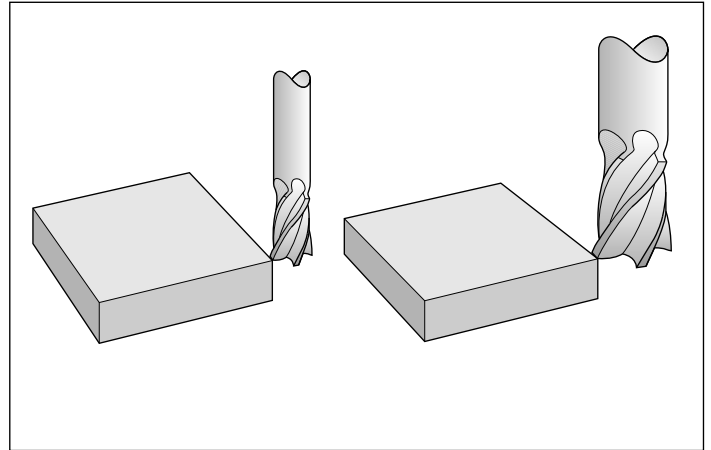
Die TNC berücksichtigt Länge und Radius des Werkzeugs
